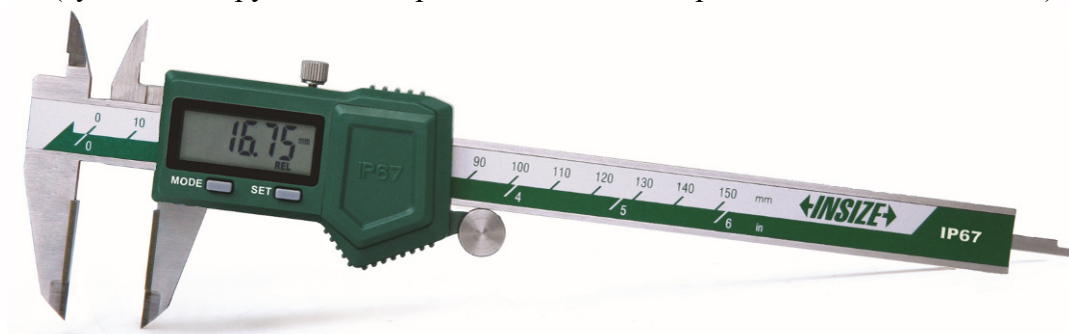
Общий вид штангенциркулей модификации 1110
